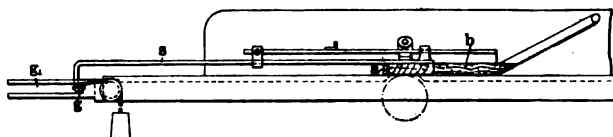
Schutzvorrichtung für Abrichtobelmaschinen.
